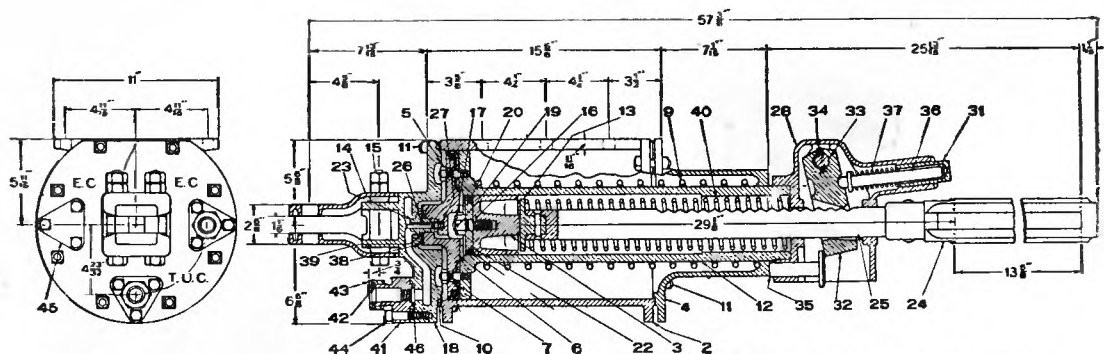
Тормозной цилиндр (груженный) с храповым приспособлением для двухрежимного оборудования.
